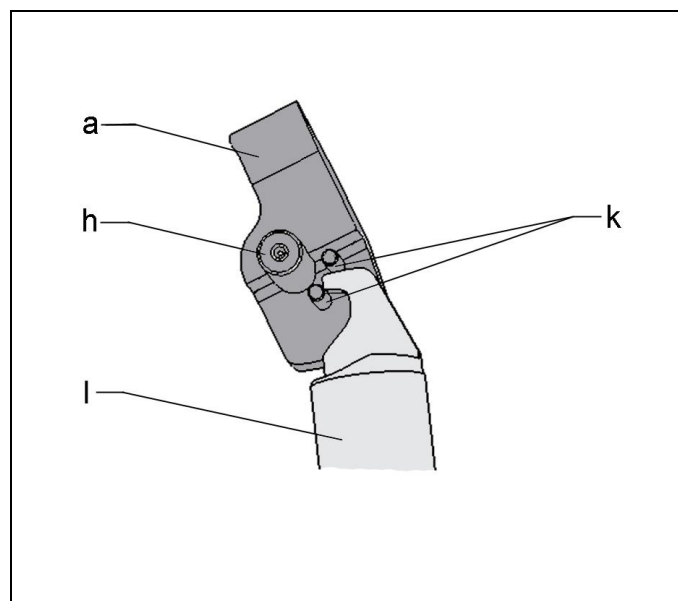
Desmontaje / montaje de la palanca de sujeción
